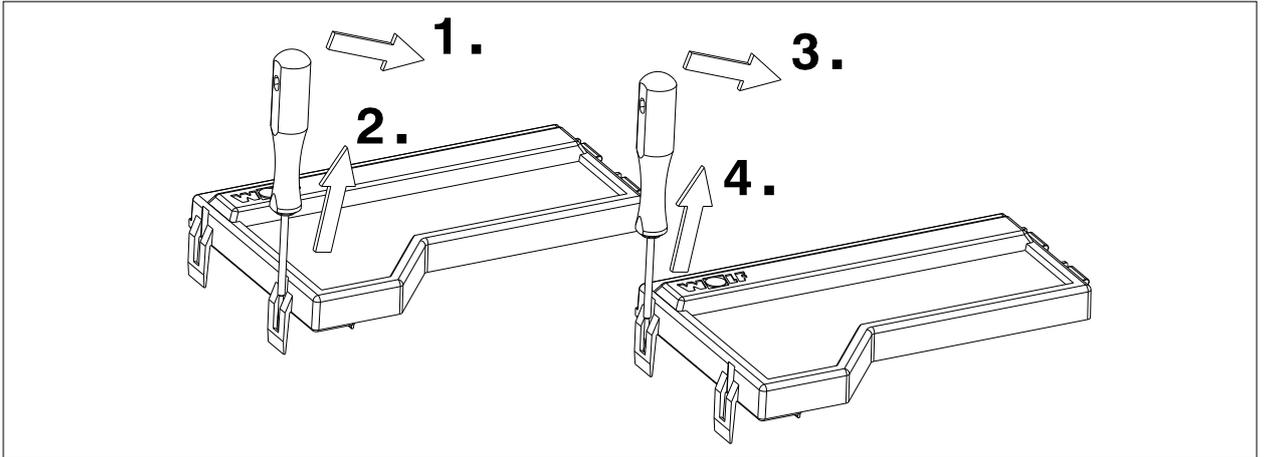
Gehäusedeckel HCM-2 entfernen
